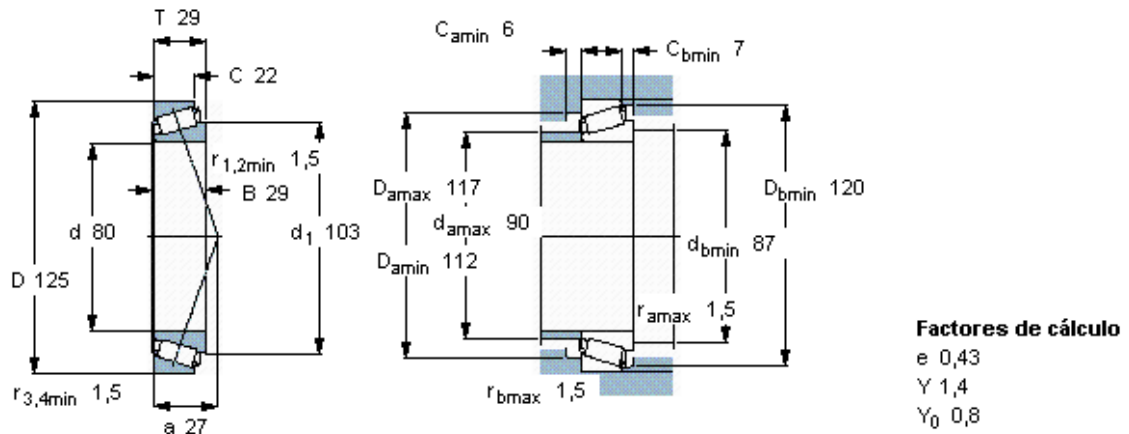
Dimensiones del Rodamiento SKF 32016.
